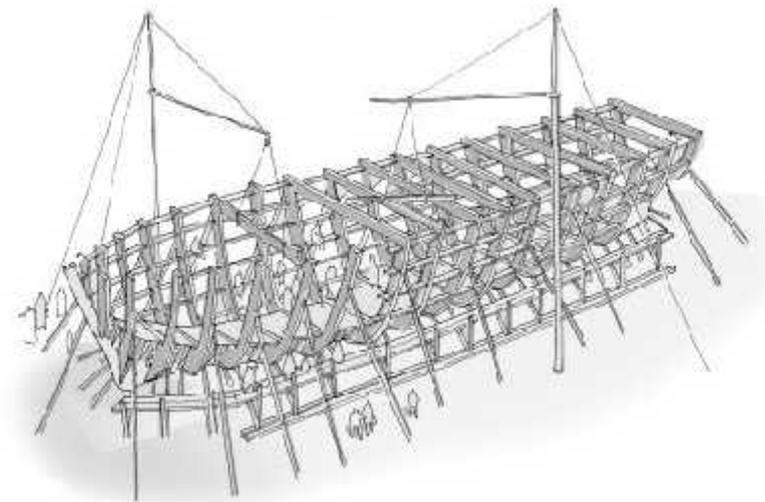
Construcción de un barco por el sistema de remaches.
